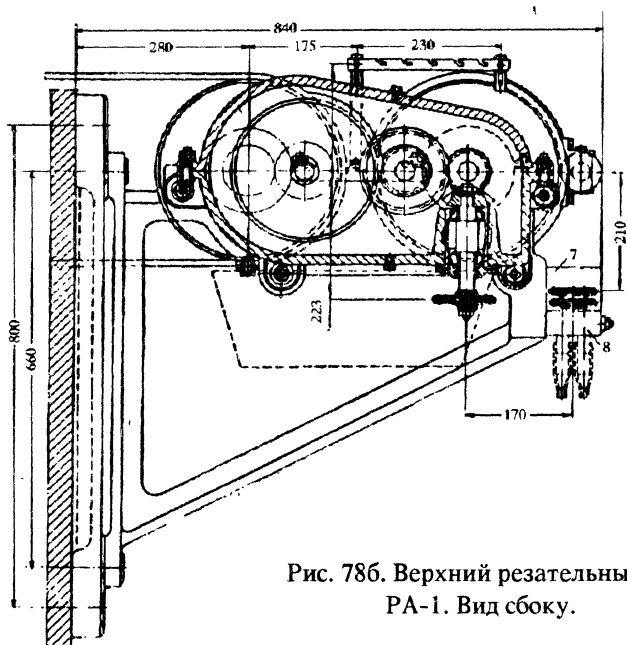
Верхний резательный станок РА-1. Вид сбоку.
